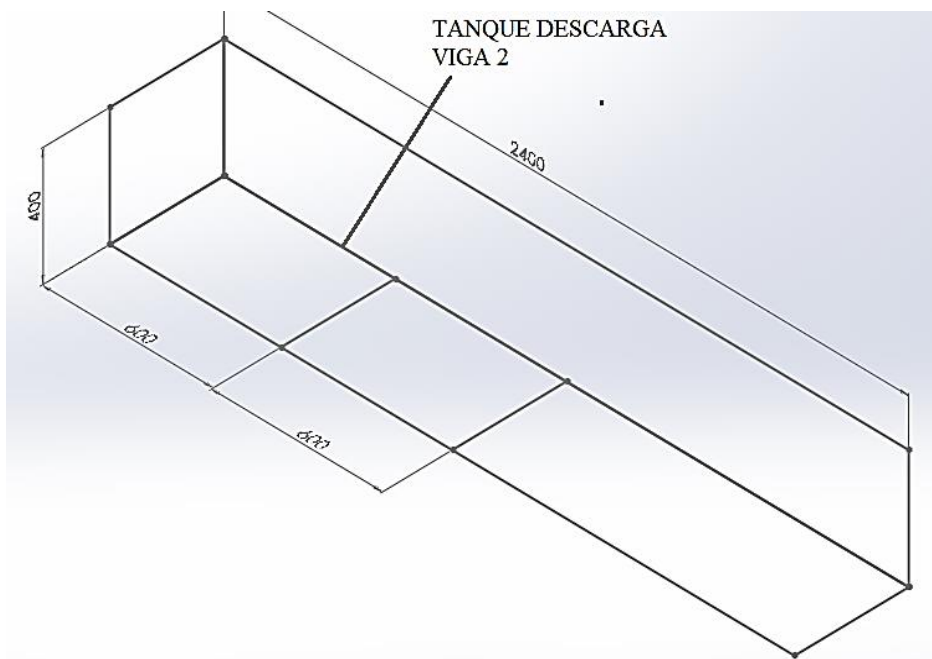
Viga 2 Ángulo (1 * 1 * 1/8) in
